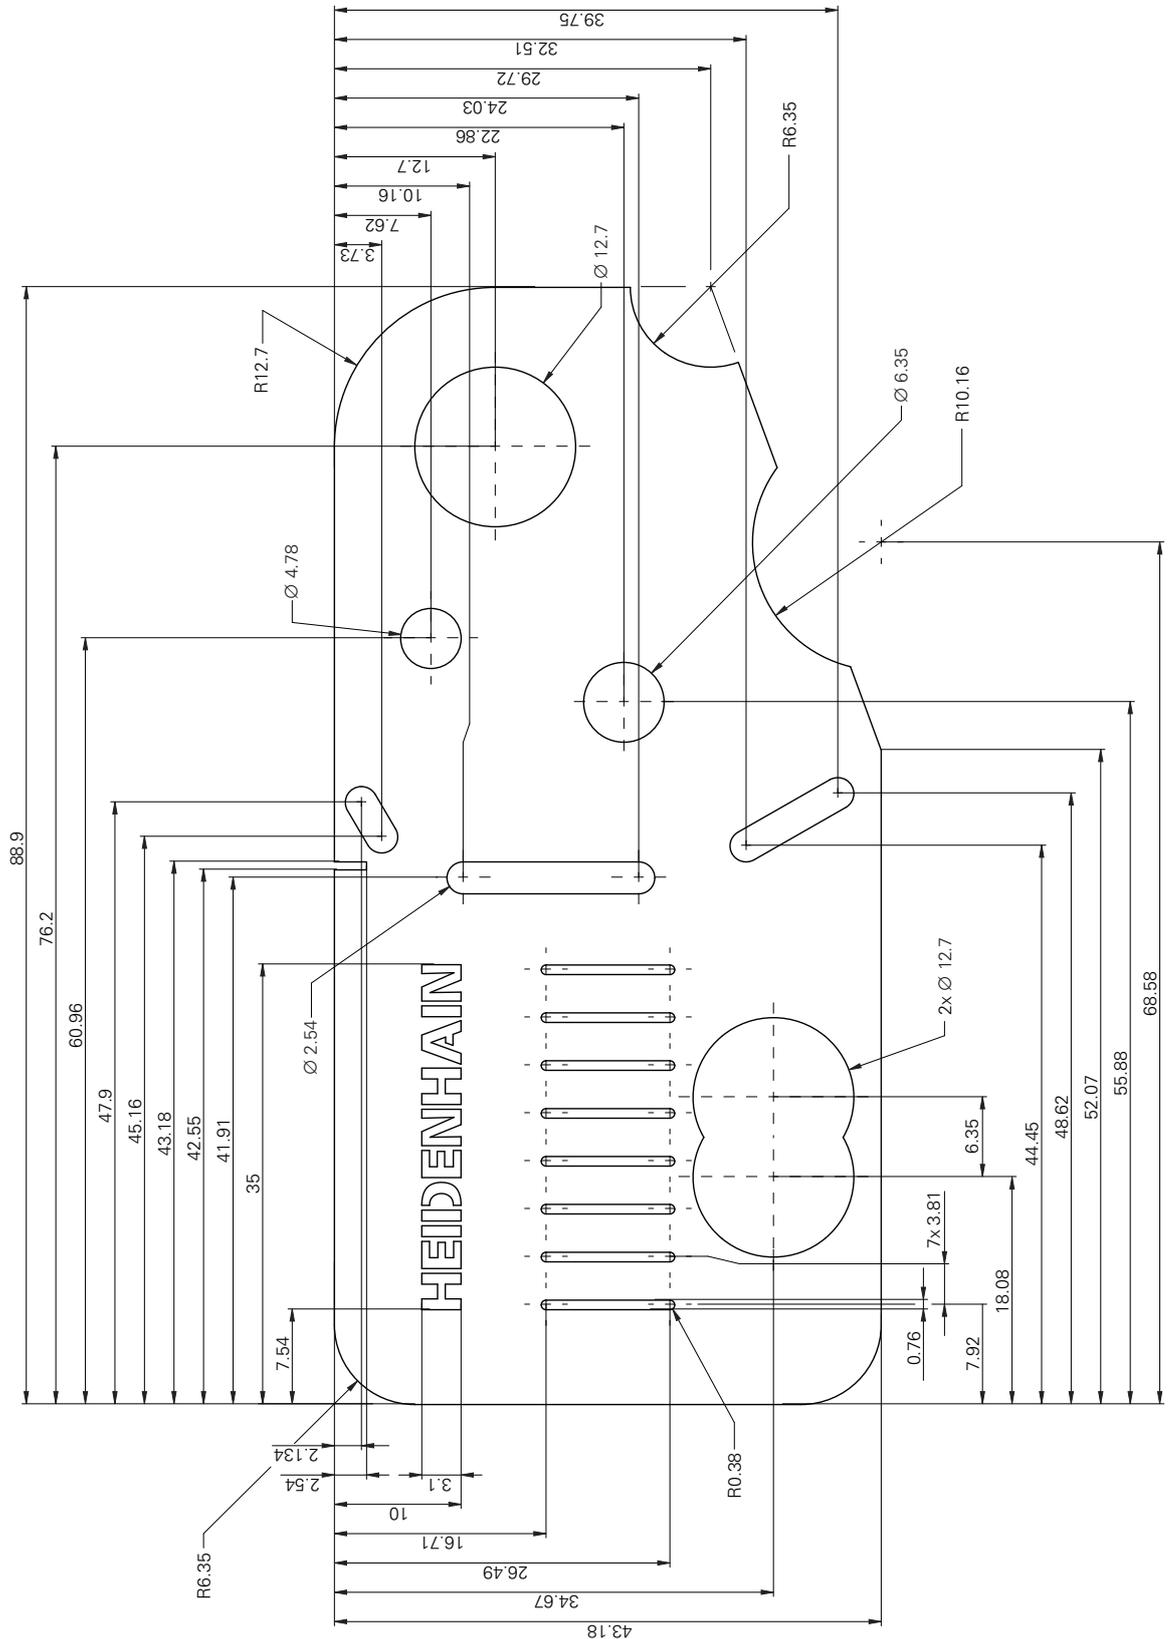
Dimensiones del aparato con soporte Multi-Pos
